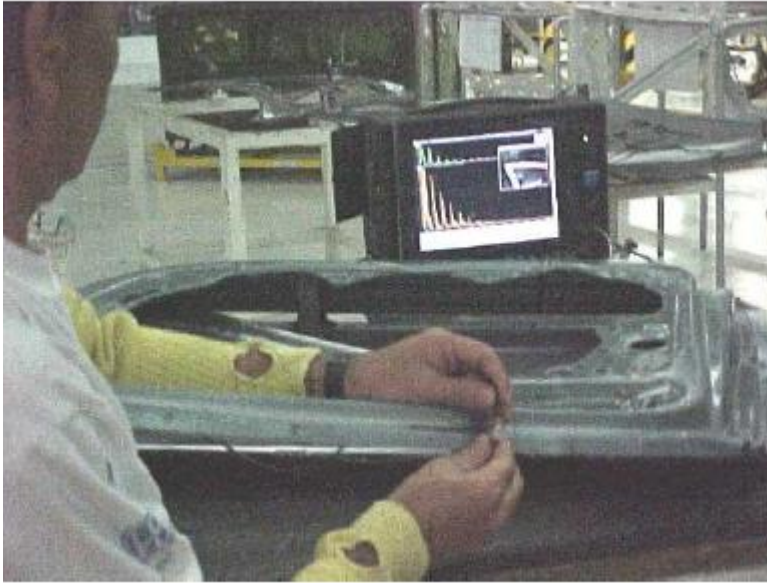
Proceso de verificación puntos de soldadura en VW Navarra
